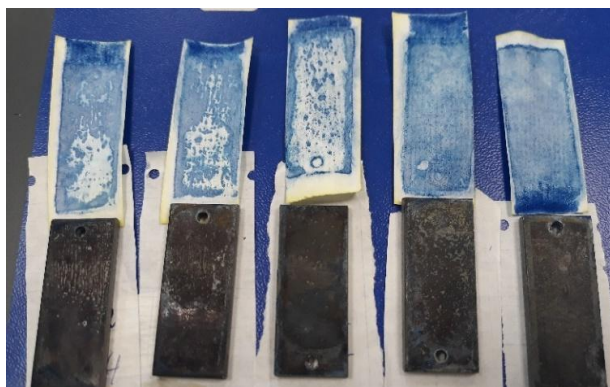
Индикаторы поверхности образцов с неподготовленной поверхностью
